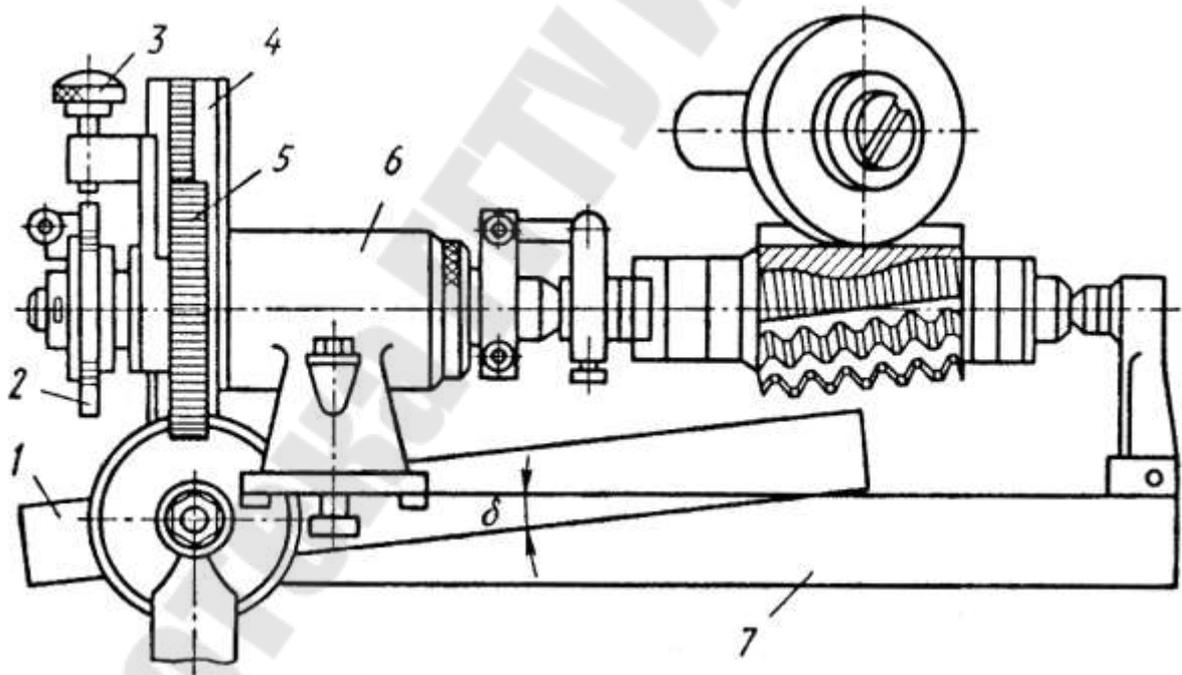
Приспособление для заточки червячных фрез на универсально-заточном станке: 1 – копирная линейка; 2 – делительный диск; 3 – фиксатор; 4 – рейка; 5 – шестерня; 6 – бабка изделия; 7 – стол станка.
